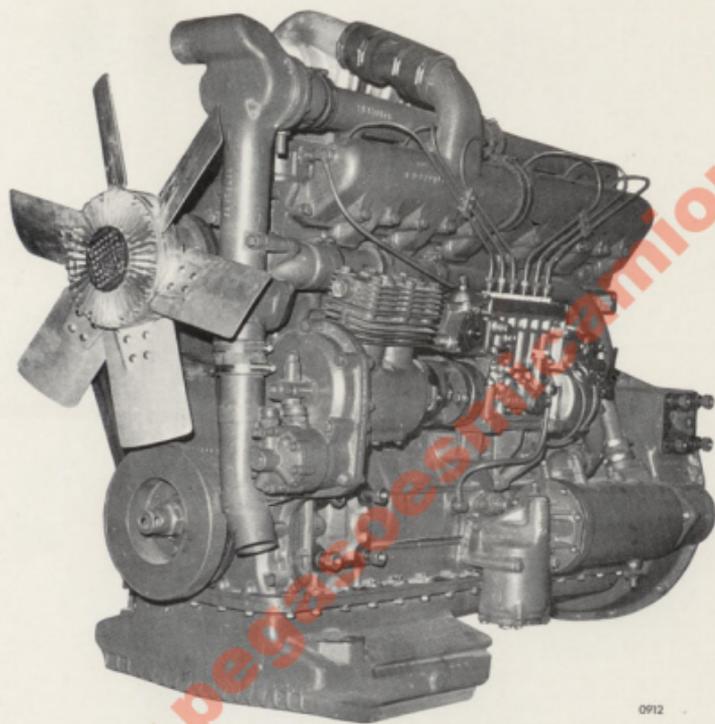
Motor 9156, lado derecho (Montaje HASTA)
